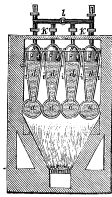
Green's patentirte Dampfhebel-Construction. Querschnitt.
